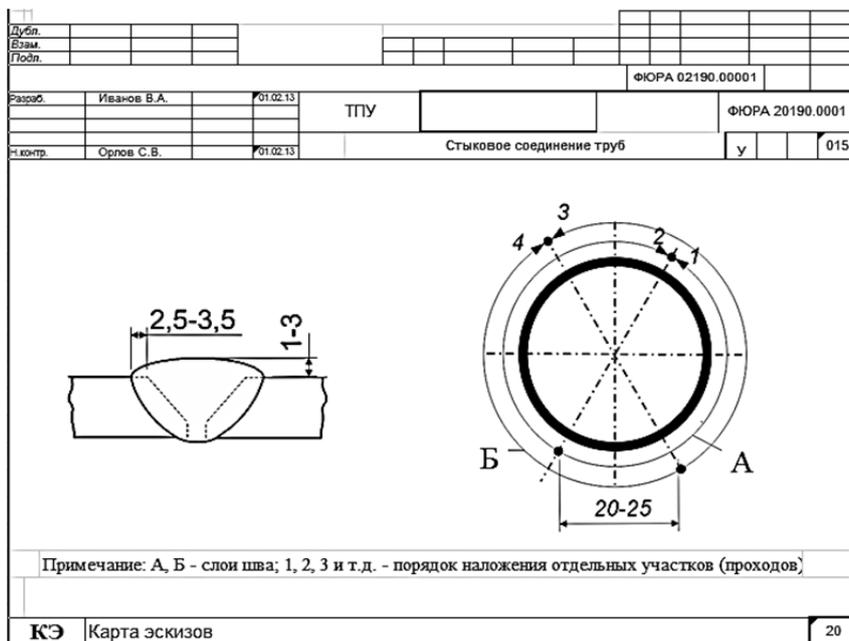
Пример оформления карты эскизов к сварочной операции
